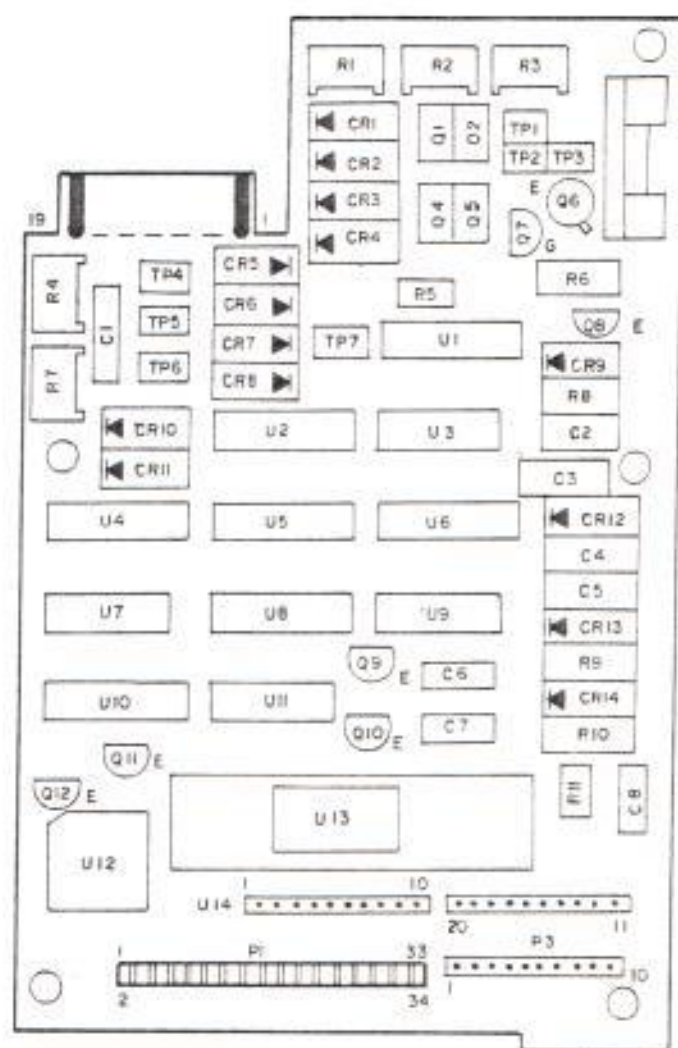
LOCALIZACION DE LOS COMPONENTES EN LA TARJETA PRINCIPAL
